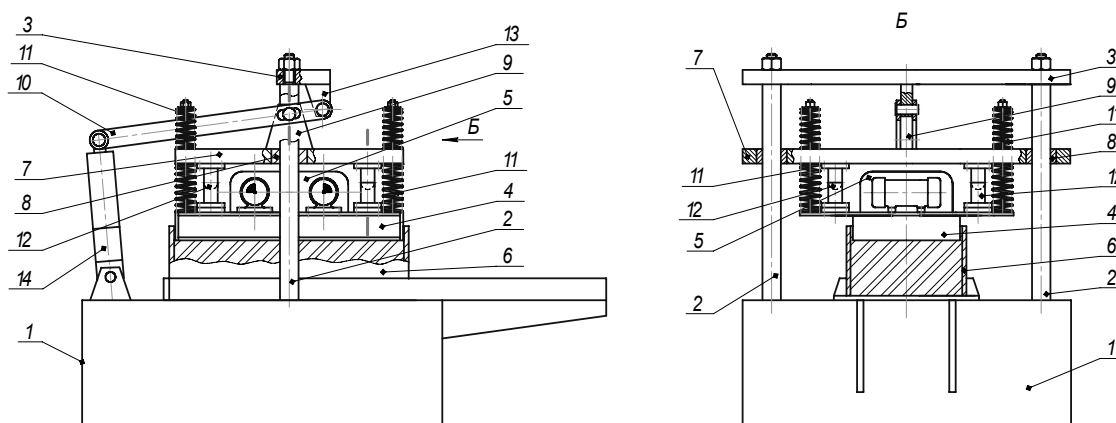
Общий вид вибрационного пресса для формования изделий из металлических порошков:
